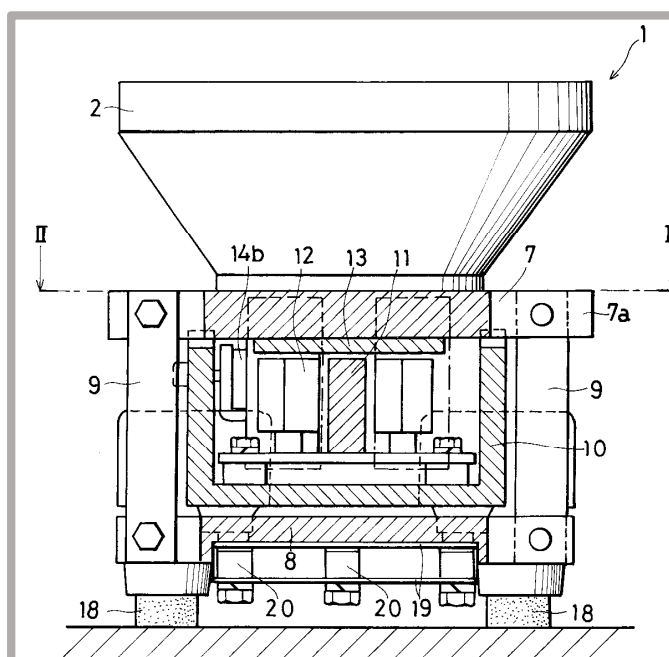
Zásobník se spirálovou drážkou [5]
